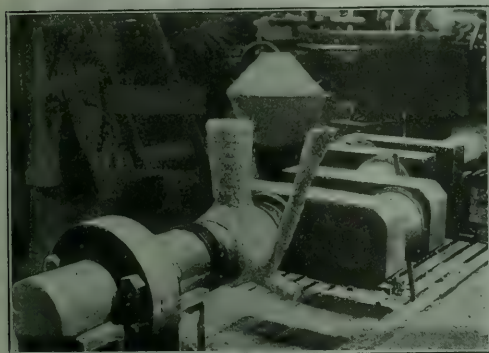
SOLDADURA DE TERMITA EN EL CIGÜEÑAL ANTES DE QUITAR EL PILÓN Y LAS MAZAROTAS
